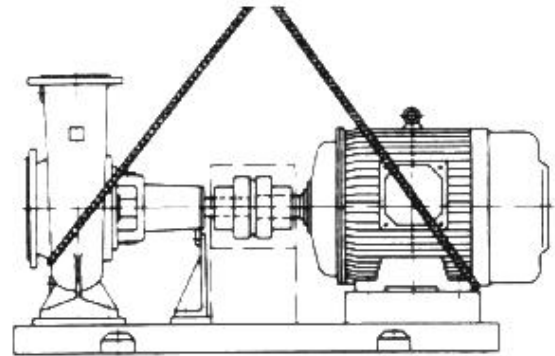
Bomba y máquina de accionamiento sobre placa de base común.
